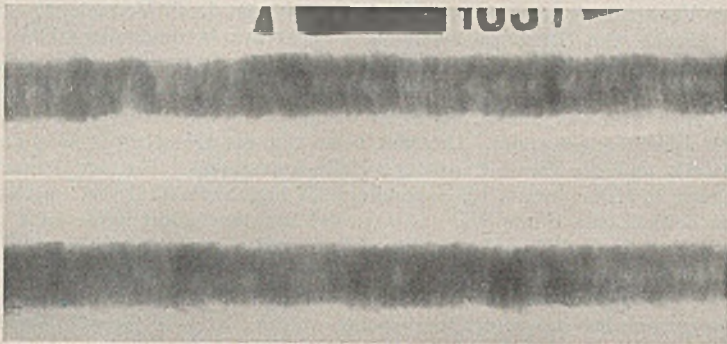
Röntgenaufnahmen eines auf der Baustelle in vertikaler Lage geschweißten Hauptträgerstoßes der Brücke über die Müggelspree.
